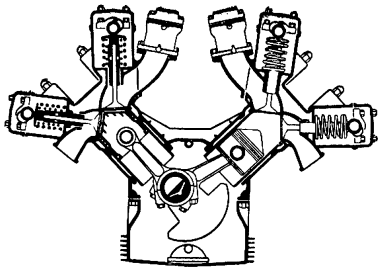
Схематический разрез двигателя автомобиля «Феррари»
